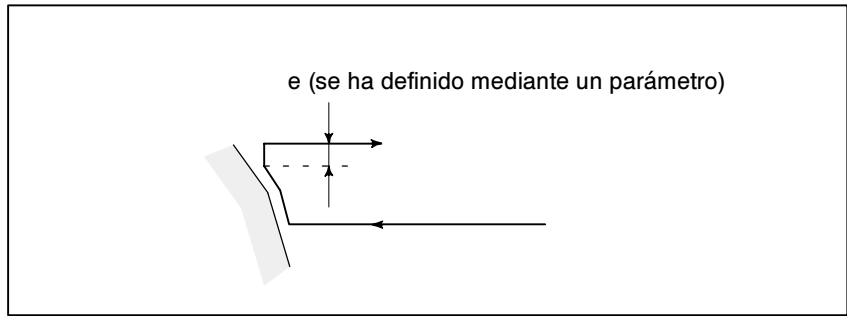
(e) Achaflanado en arranque de material en torneado (Tipo II)
